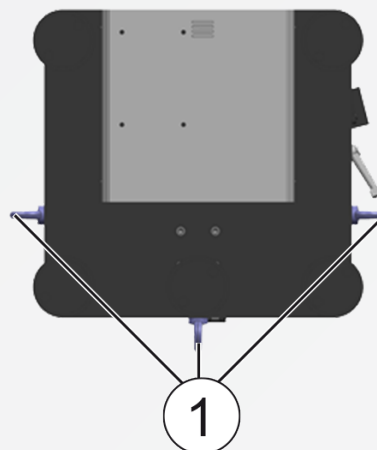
Ansicht von unten: Aufnahmepunkte (1) für Ringschrauben
